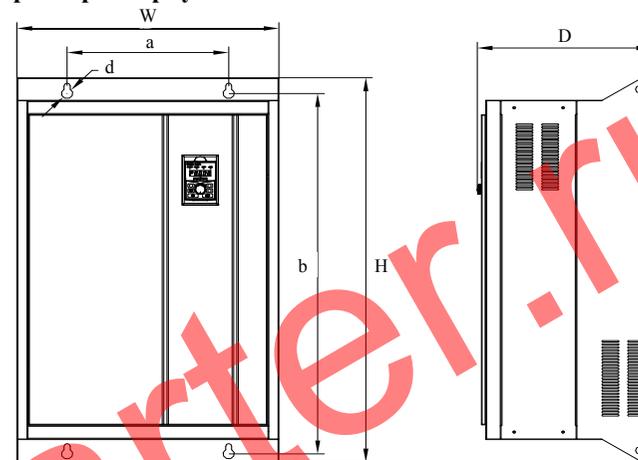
Внешний вид корпусов типоразмеров 4 - 11 (навесное исполнение)
